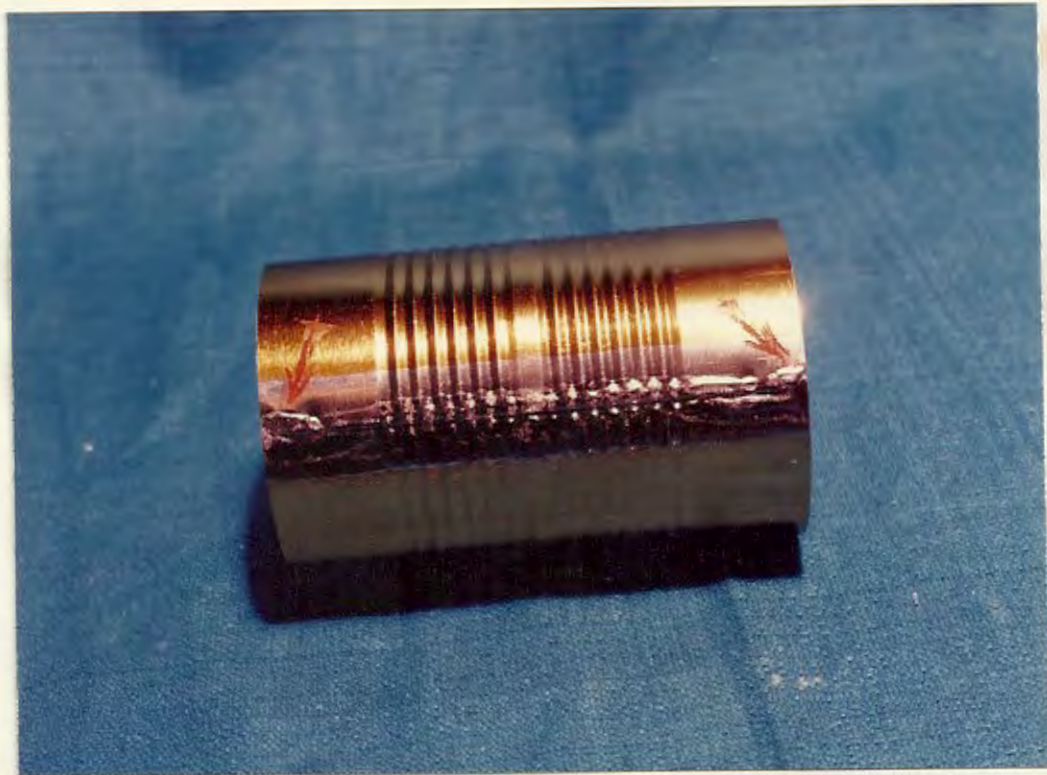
Exceso de soldadura sobre solapa.
